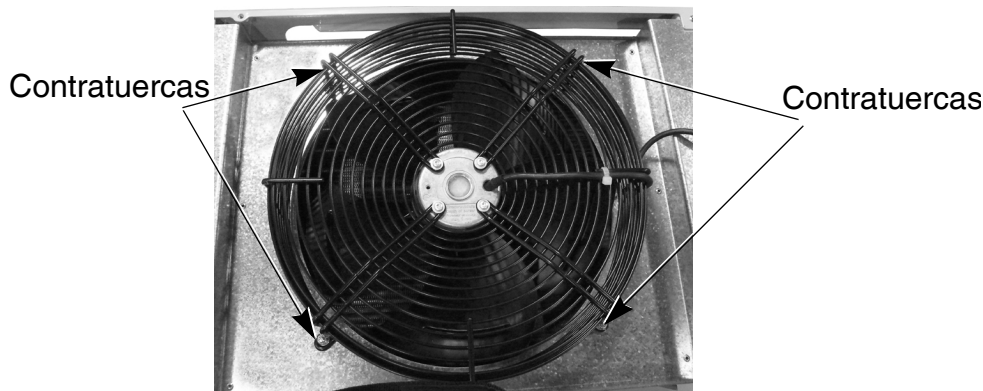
Tuercas De Montaje Del Ventilador Condensador
